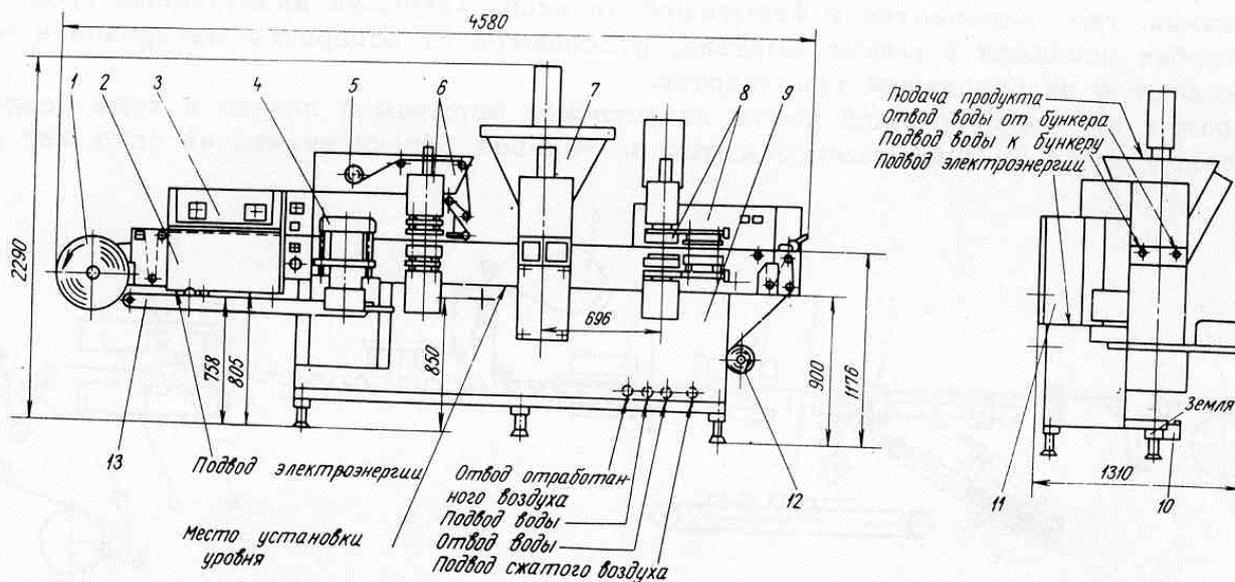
Общий вид автомата фасовочно-упаковочного марки М6-ОРК: 1 – барабан; 2 – механизм протягивания пленки; 3 – пульт управления; 4 – штамп; 5 – рулонодержатель для запечатывающего материала; 6 – механизм запечатывания; 7 – дозатор; 8 – механизм формования коробок; 9 – рама; 10 – планка для аварийной остановки автомата; 11 – шкаф электрооборудования; 12 – рулонодержатель для упаковочной пленки; 13 – транспортер
